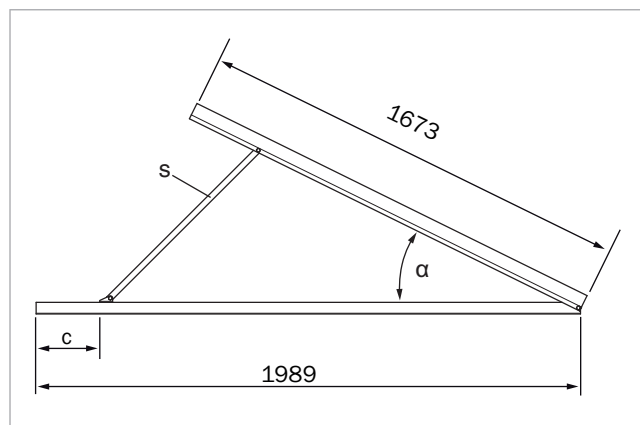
suporte para telhado plano, dimensões e ângulo de montagem
